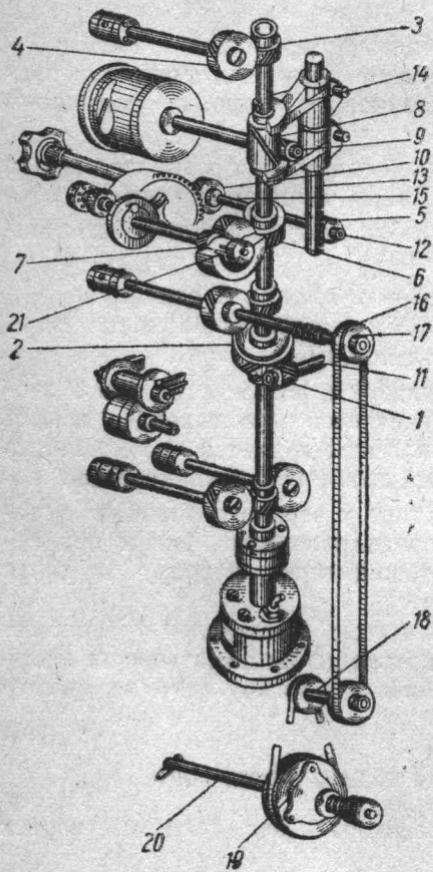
Кинематическая схема проектора: 1—10 — шестерни; 11 — ведущий вал; 12 — шестерня; 13 — рейка; 14 — вилка; 15, 16 — валы; 17, 19 — шкивы; 18 — промежуточный вал; 20 — вал нижней катушки; 21 — маховик
